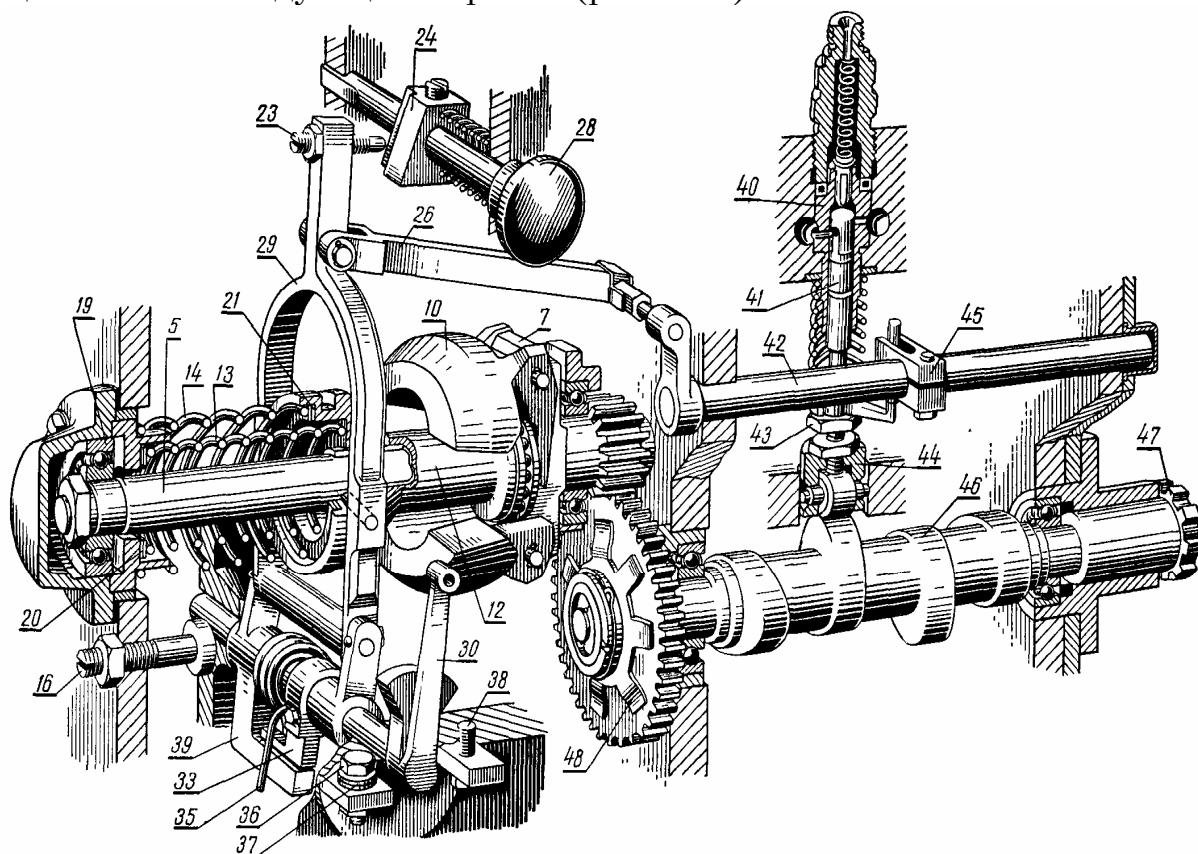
Схема действия регулятора типа РВ с насосом 4ТН-8,5×10: 40 – втулка плунжера; 41 – плунжер; 42 – рейка; 43 – регулировочный болт толкателя; 44 – корпус толкателя плунжера; 45 – хомутик рейки; 46 – кулачковый вал; 47 – шлицевая втулка; 48 – фрикционная муфта (названия остальных позиций те же, что и на рис. 4.34)
